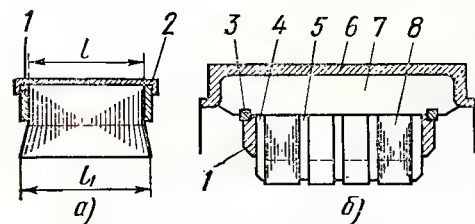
Статорный сердечник, скрепленный скобами (а) и набранный в станину (б)
